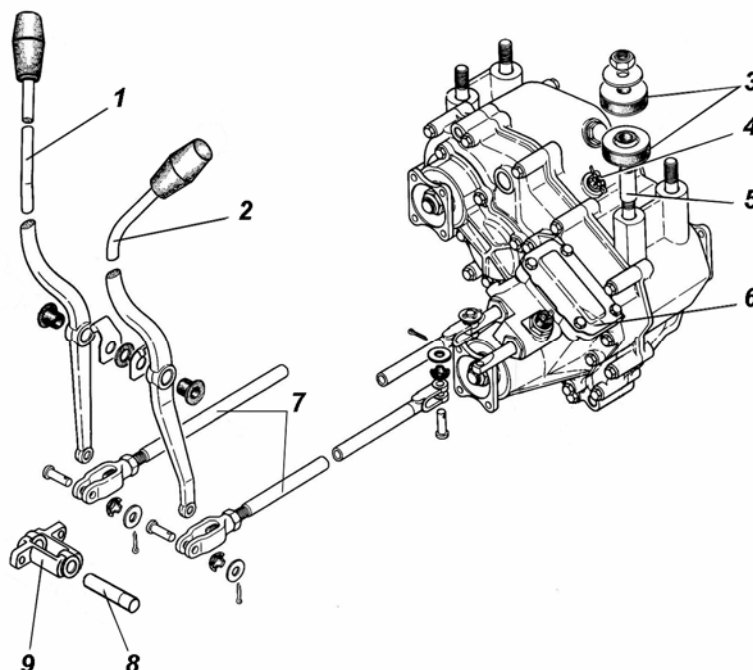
Раздаточная коробка и ее привод: 1 – рычаг включения передач; 2 – рычаг включения блокировки дифференциала; 3 – подушки; 4 – гайка; 5 – втулка; 6 – крышка люка; 7 – тяги; 8 – ось рычагов управления; 9 – кронштейн рычагов управления
